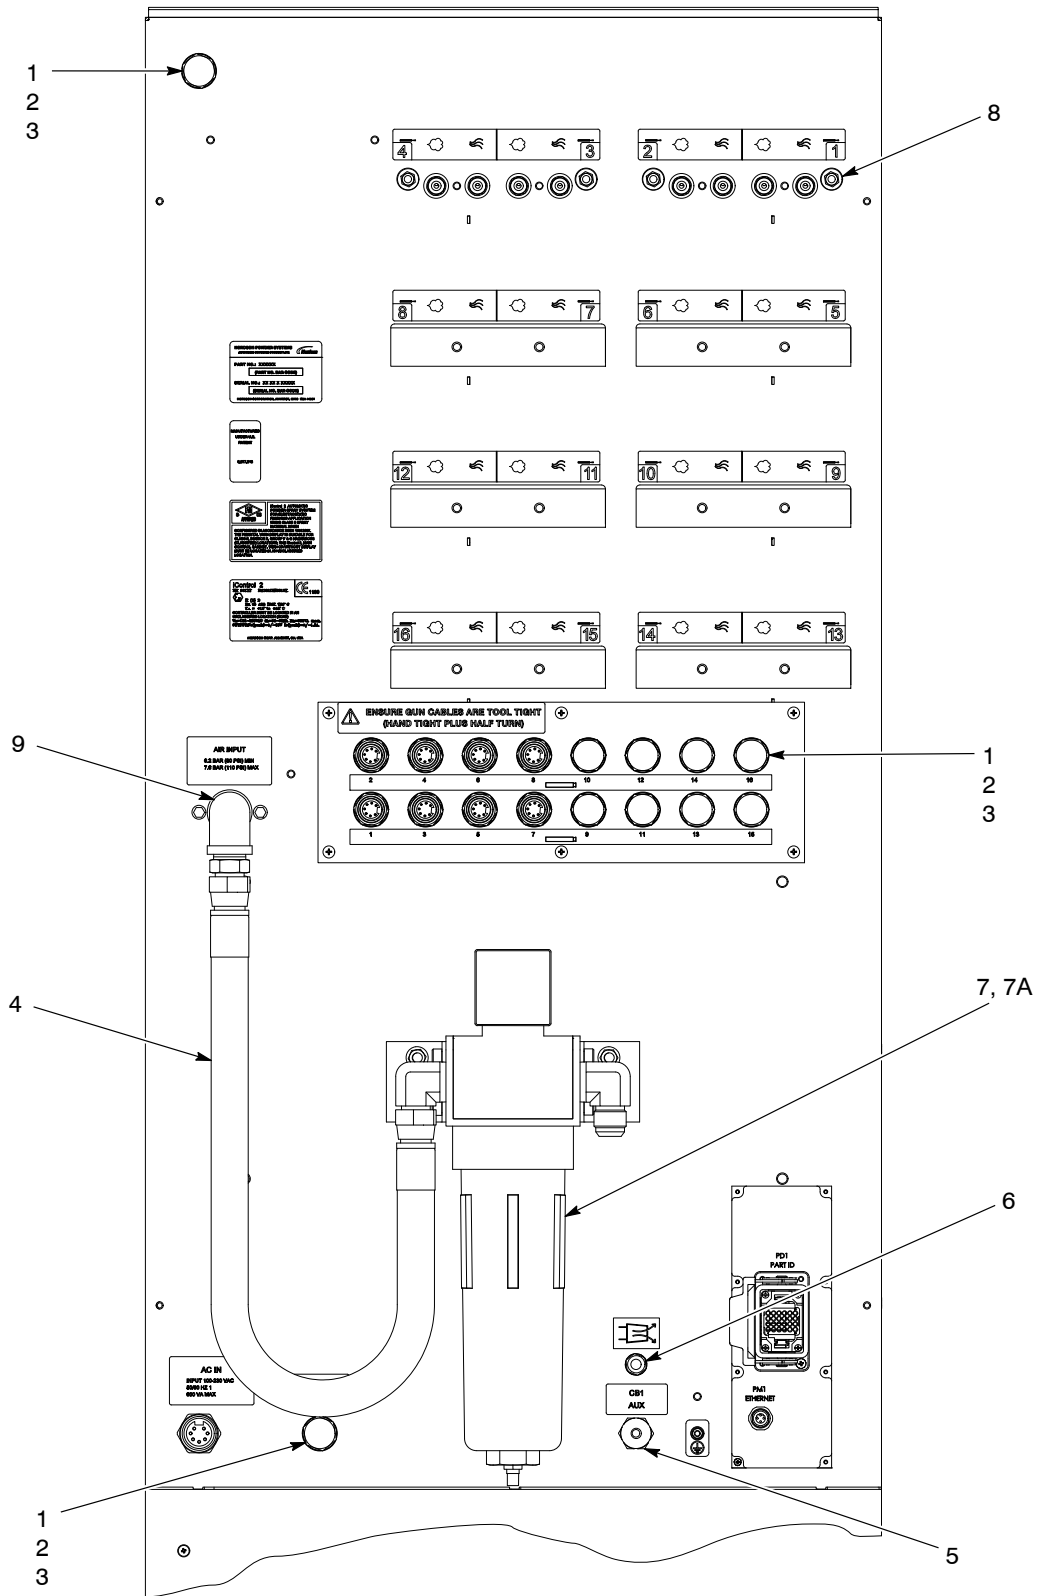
Piesele consolei principale și auxiliare - vedere din spate (1 din 3)
